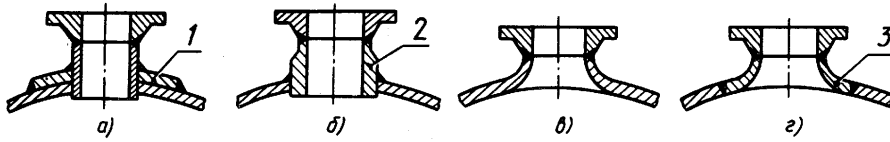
Способы соединения люков и штуцеров с корпусами аппаратов
